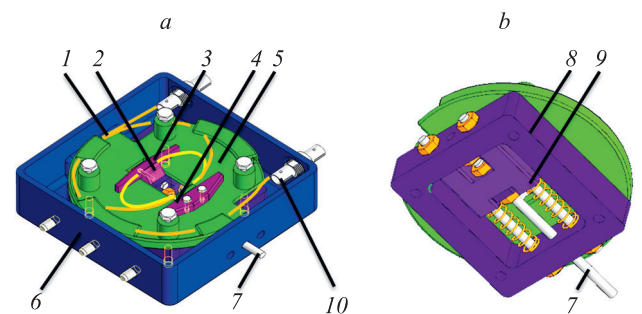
Схема чувствительного элемента датчика смещения: вид в корпусе сверху (a) и без корпуса снизу (b). 1 — оптоволокну, чувствительное к изгибам; 2, 3 и 4 — подвижные и неподвижный упоры (рис. 1); 5 — неподвижный упор, круглый стол; 6 — корпус датчика; 7 — активатор; 8 — рама; 9 — подвижная каретка, передающая смещение с активатора к подвижным упорам 2 и 3; 10 — оптические розетки
